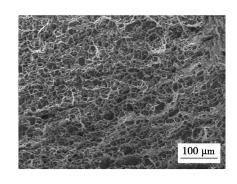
焊缝拉伸断口微观形貌 Fig. 4 Tensile fracture morphologies of FSW joint
